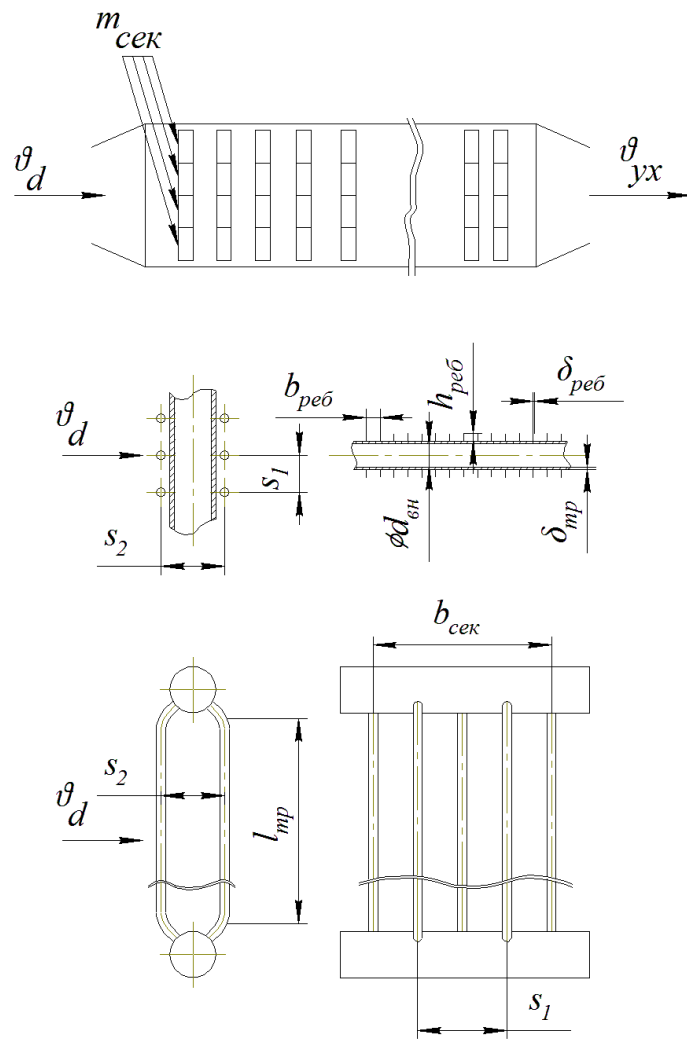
Конструктивные параметры типовой секции поверхностей нагрева КУ
